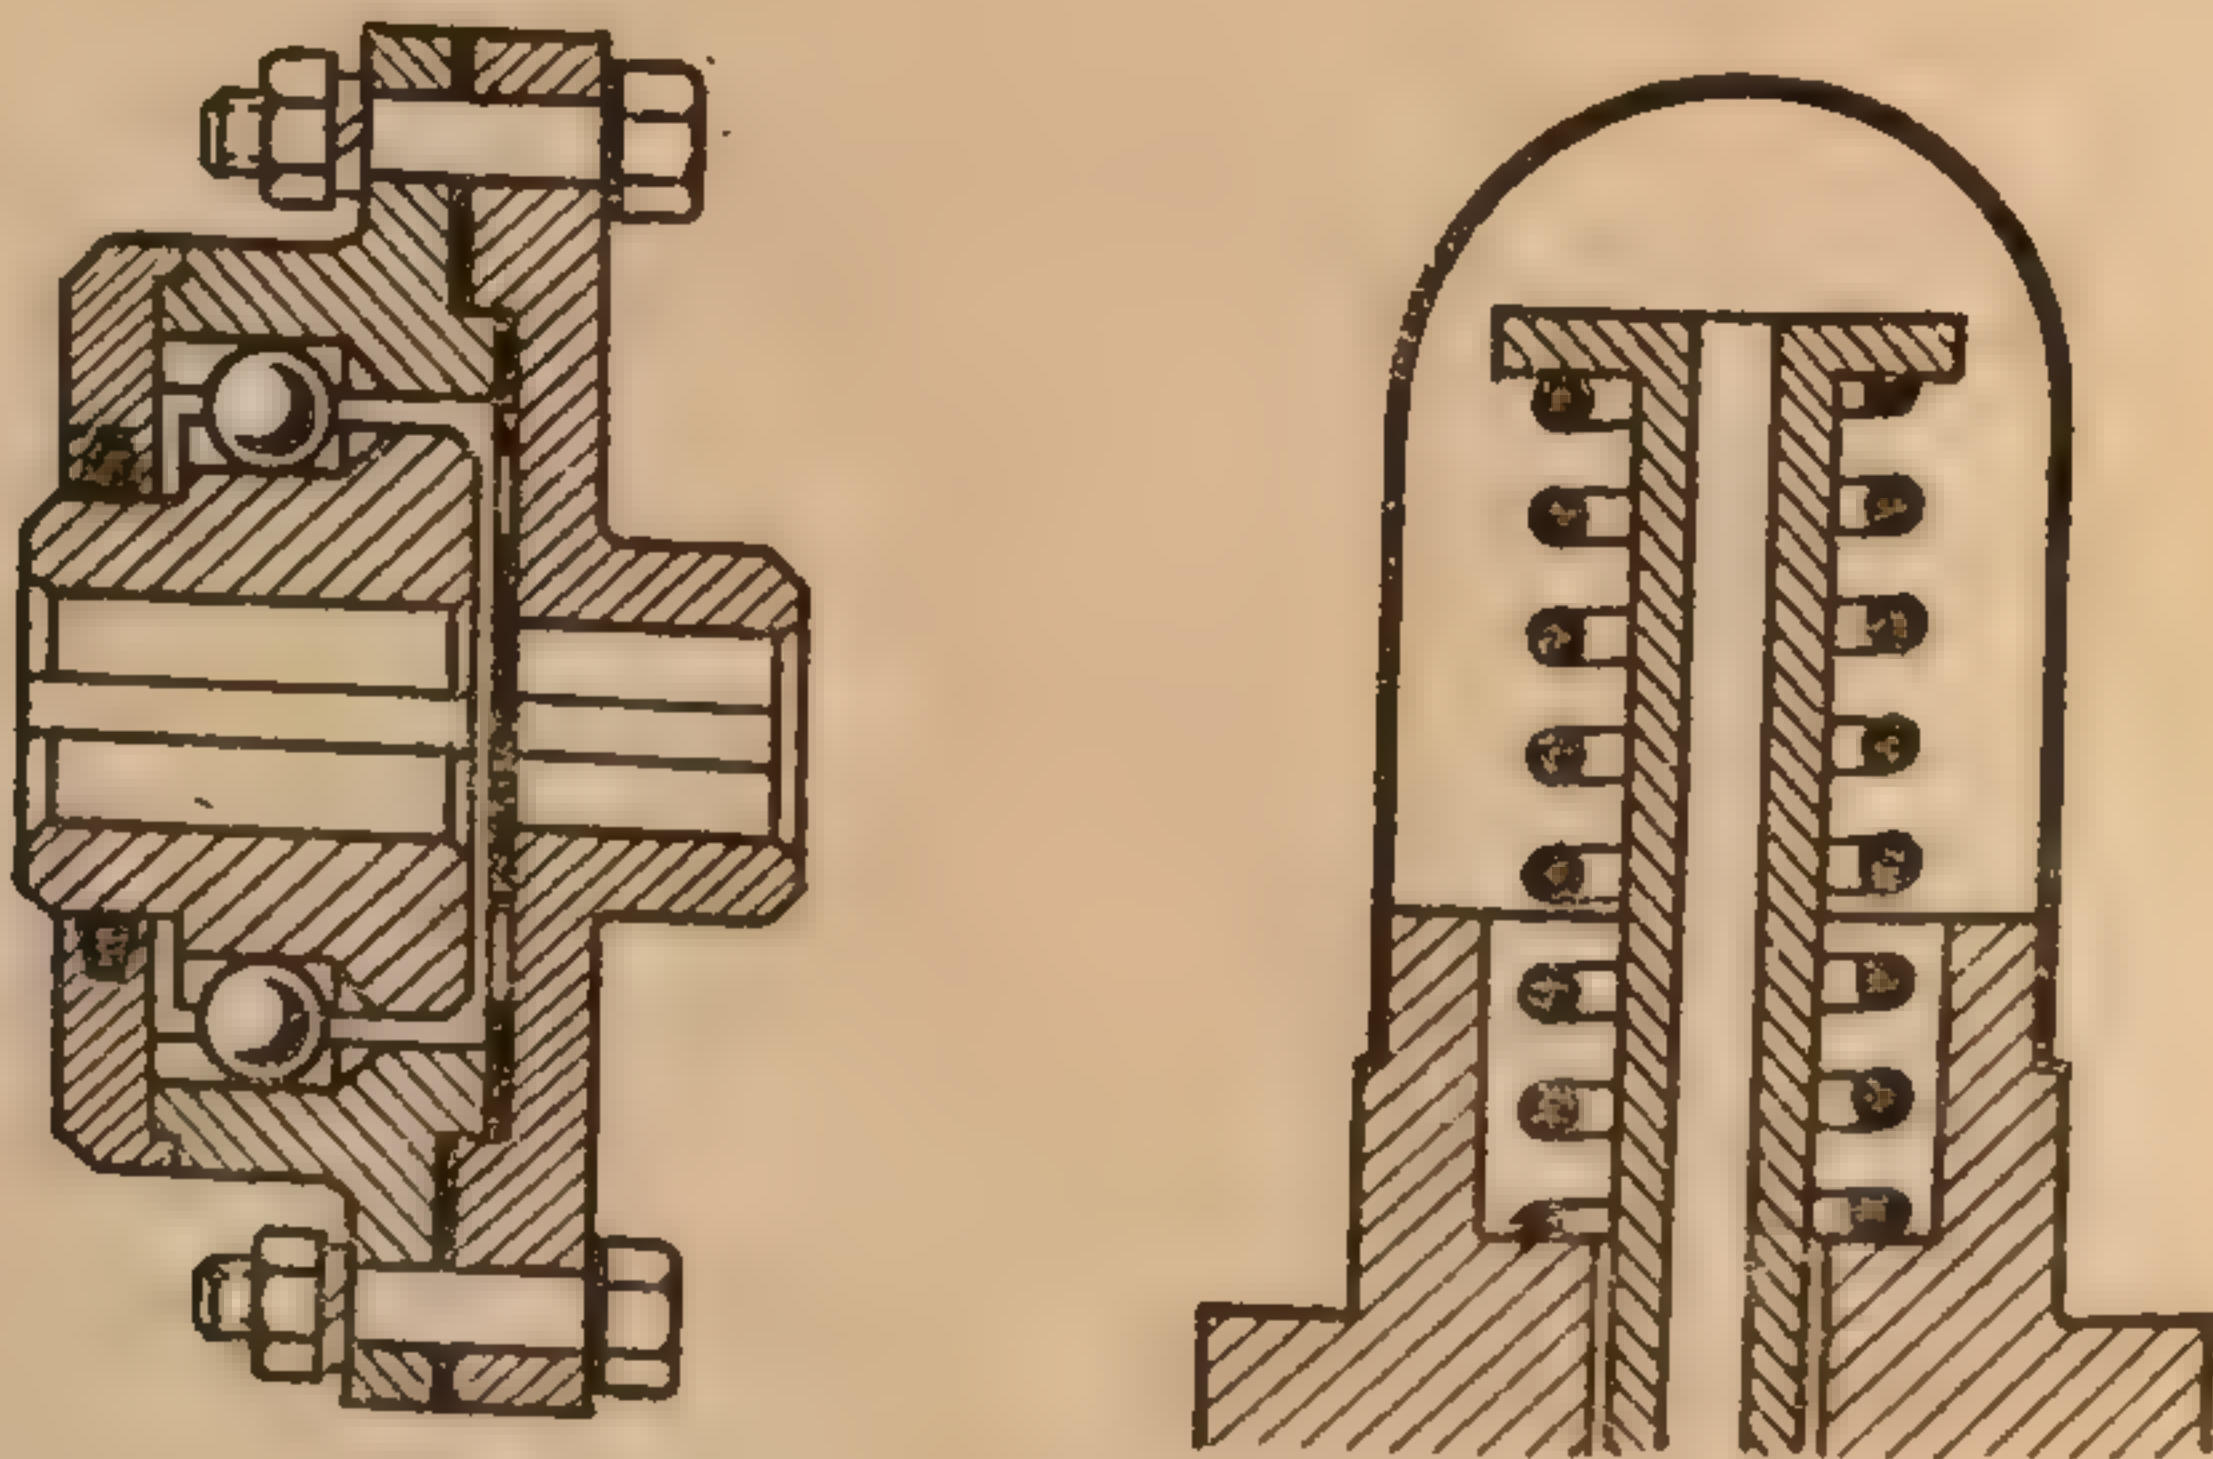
Примеры допустимой заливки деталей чертежа тушью
